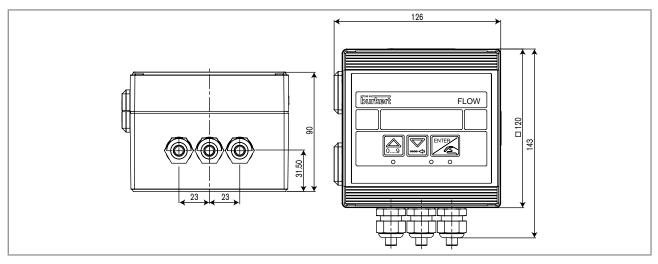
Abmessungen des Transmitters 8025 Universal, Wandmontage-Ausführung [mm]
